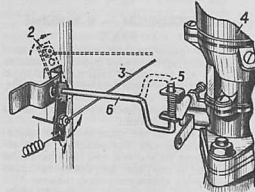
Установка карбюратора К-59В на двигатель автомобиля «Москвич-402» взамен карбюратора К-44: 1 — новое положение рычага привода; 2 — старое положение рычага привода; 3 — трос привода; 4 — карбюратор К-59В; 5 — рычаг дросселя; 6 — соединительная тяга.
